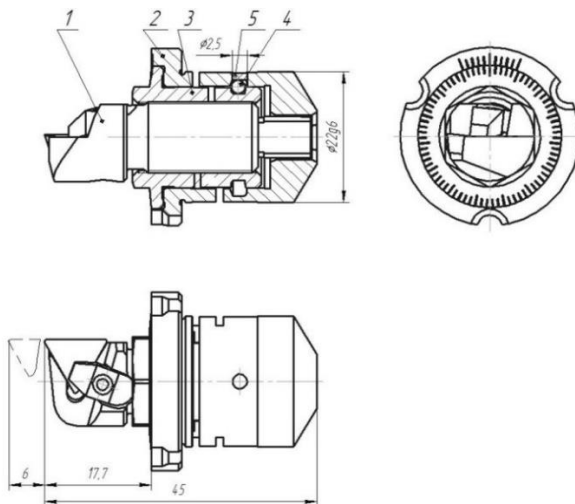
Резцовая вставка с креплением режущей пластины прихватом
